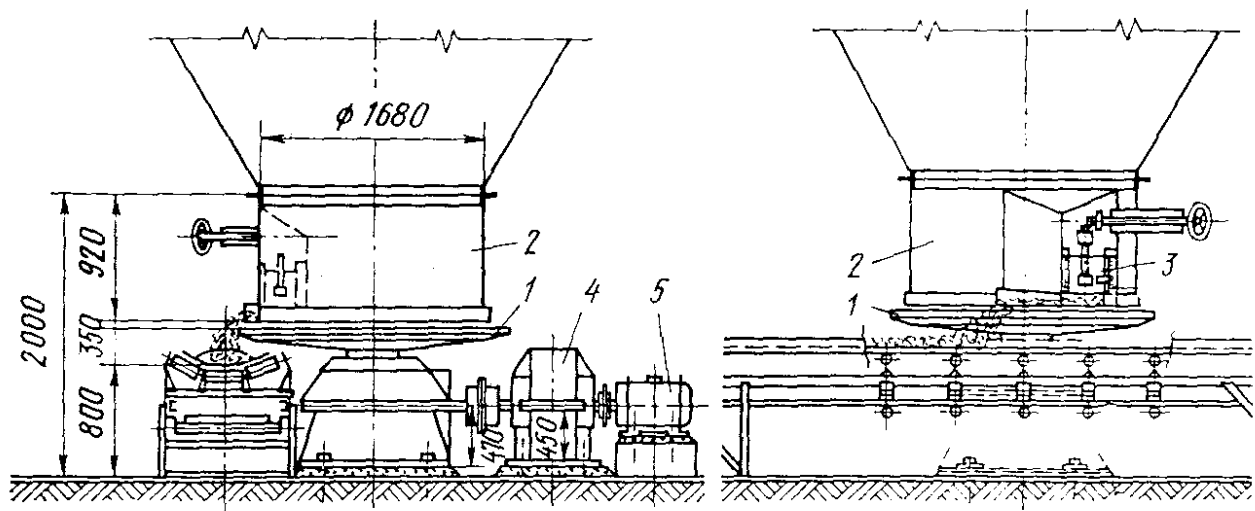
Загальний вид установки тарілчастого живильника в шихтовому відділенні: 1 - таріль, що обертається; 2 – корпус живильника; 3 – шибер; 4 – електродвигун; 5 – редуктор
